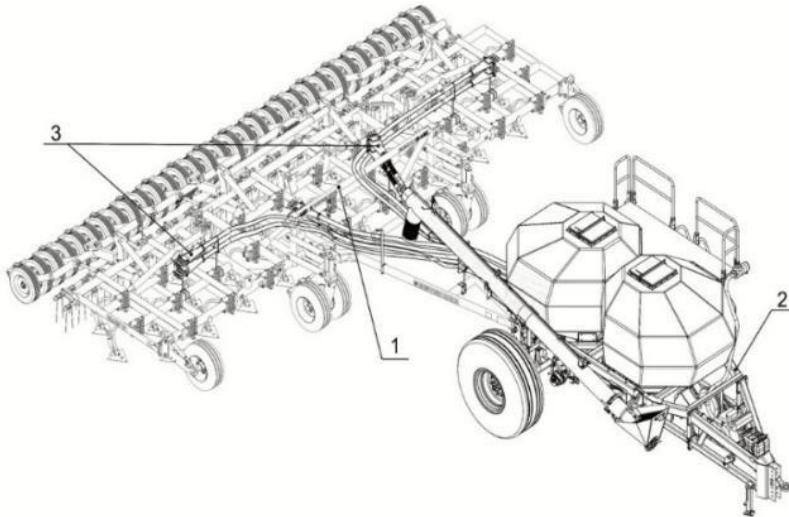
Загальний вигляд сівалки-культиватора пневматичної широкозахватної ALCOR 7,5: 1 – культиваторна частина; 2 – посівна частина; 3 – пневматична частина.
